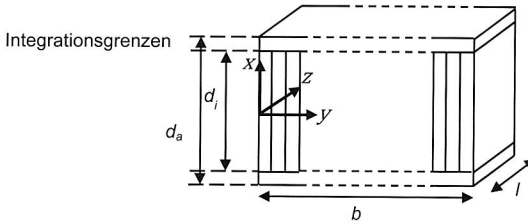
Geometrische Definition des beidseitig verbundenen Blechpakets
